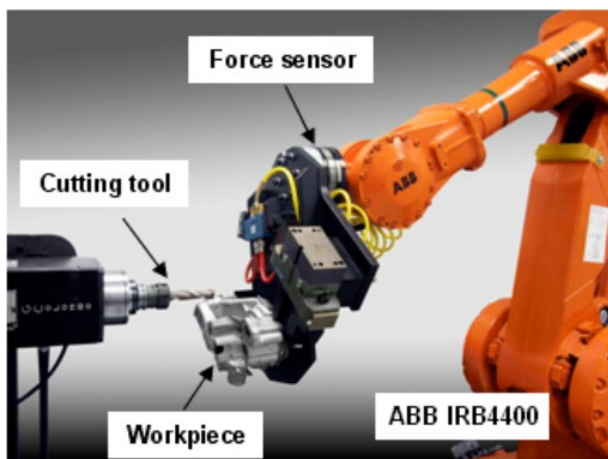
Обработка с закреплением заготовки на роботе [5]
